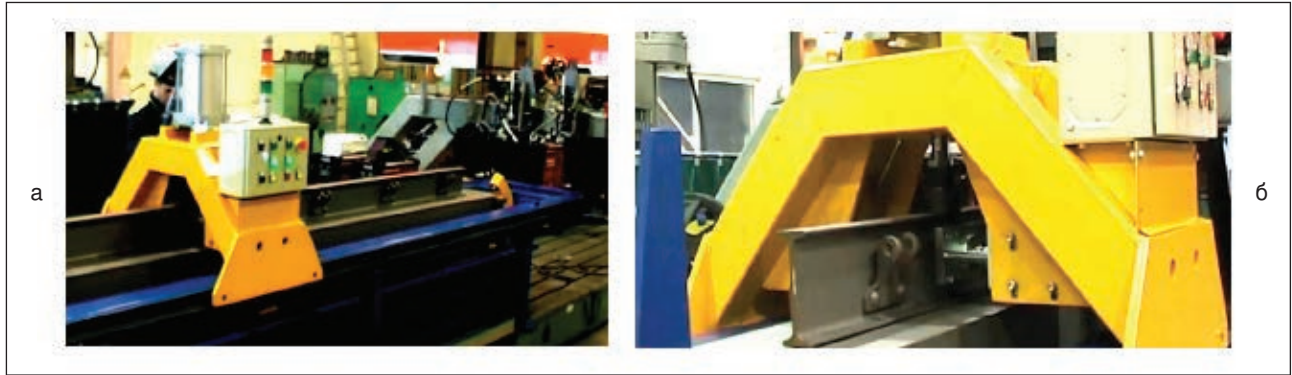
Общий вид сборочной тележки (а) со смонтированными на ней вертикальным и боковым пневмоприжимами (б)
